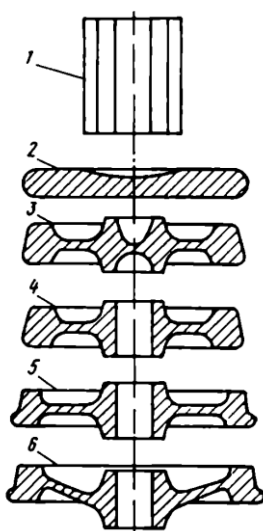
Схема деформации заготовок на заводе фирмы Bonatrans: 1 – заготовка; 2 – осадка; 3 – штамповка; 4 – прошивка отверстия; 5 – прокатка; 6 – выгибка диска и калибровка
